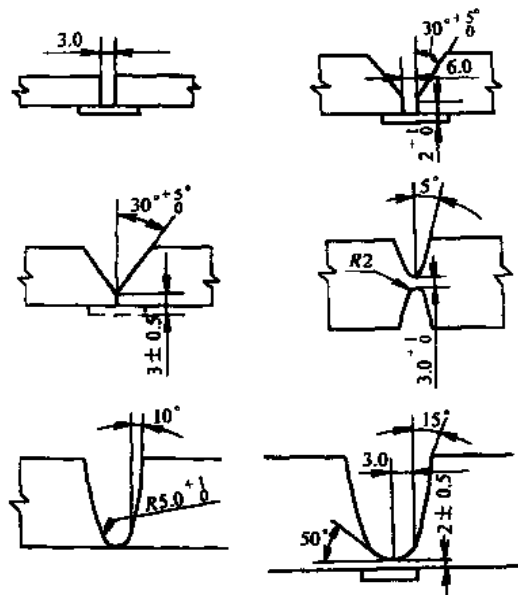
埋弧焊、MIG 焊镍基合金典型坡口形式
